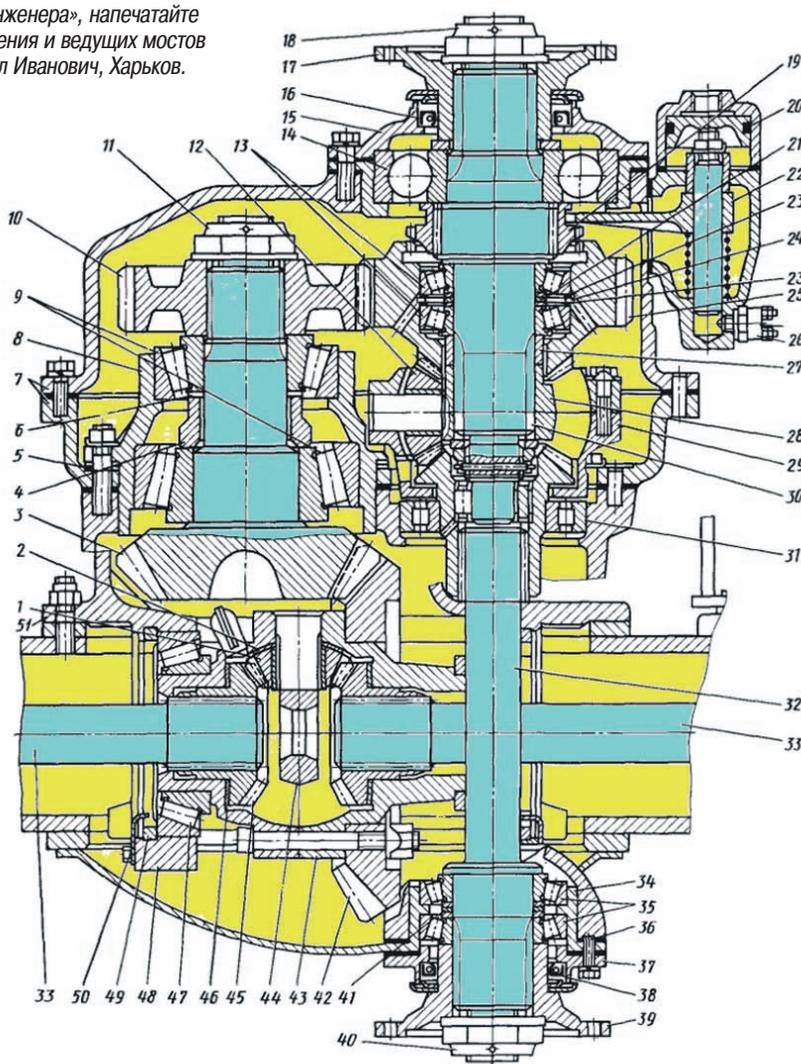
Центральный редуктор среднего моста: 1, 12 — сателлиты; 2, 46 — опорные шайбы; 3 — ведущая коническая шестерня; 4, 27 — распорные втулки; 5 — регулировочные прокладки; 6, 21, 41 — регулировочные шайбы; 7 — картеры; 8 — картер подшипников; 9, 13, 14, 31, 35, 47 — подшипники; 10 — ведомая цилиндрическая шестерня; 11, 18, 40 — гайки; 15, 37 — крышки, 16, 38 — сальники; 17, 39 — фланцы; 19 — муфта блокировки межосевого дифференциала; 20 — механизм блокировки межосевого дифференциала; 22 — вилка включения муфты; 23 — упорная шайба; 24 — стопорная шайба; 25 — ведущая цилиндрическая шестерня; 26 — датчик включения блокировки межосевого дифференциала; 28, 44 — крестовины; 29 — межосевой дифференциал; 30 — вал привода мостов; 32 — выходной вал; 33 — полуось; 34 — стакан; 36 — болт; 42 — ведомая шестерня; 43 — межосевая шестерня; 45 — полуосевая шестерня; 48 — крышка; 49 — гайка подшипника дифференциала; 50 — стопор; 51 — картер редуктора
